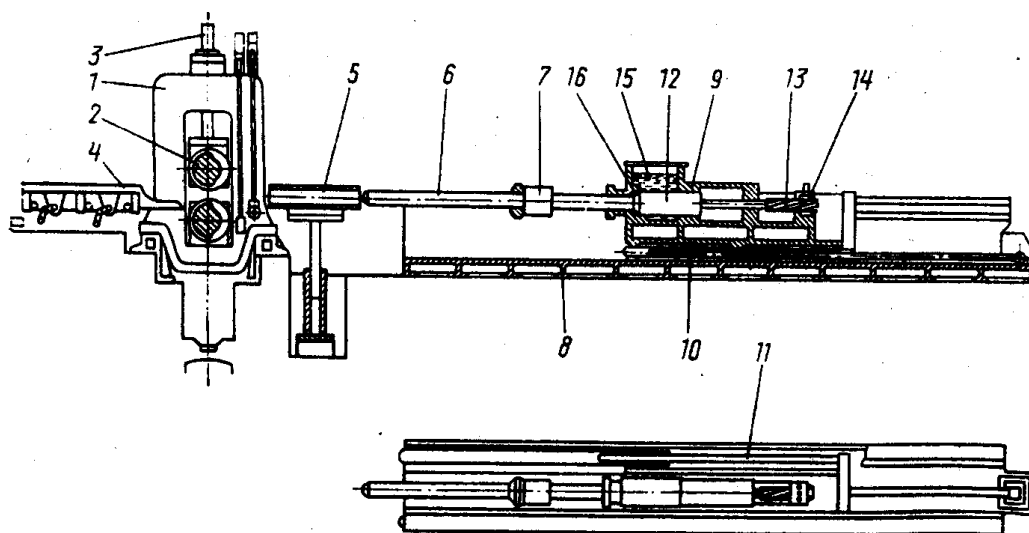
Схема стана: 1,2,3 – прокатная клетка; 4 – приемный желоб; 5 – прокатываемая заготовка; 6 – дорн; 7 – замок дорна; 9 – подающий механизм
